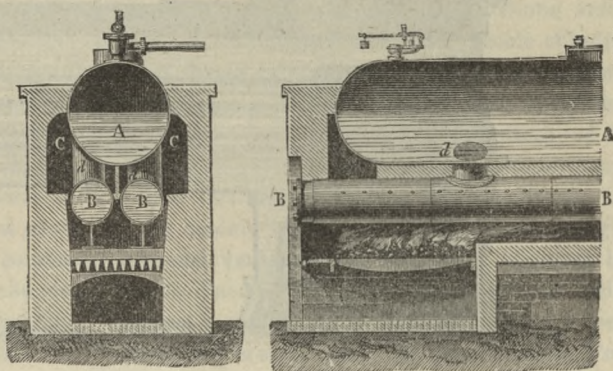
Spaccato di una caldaia di macchina a vapore.
